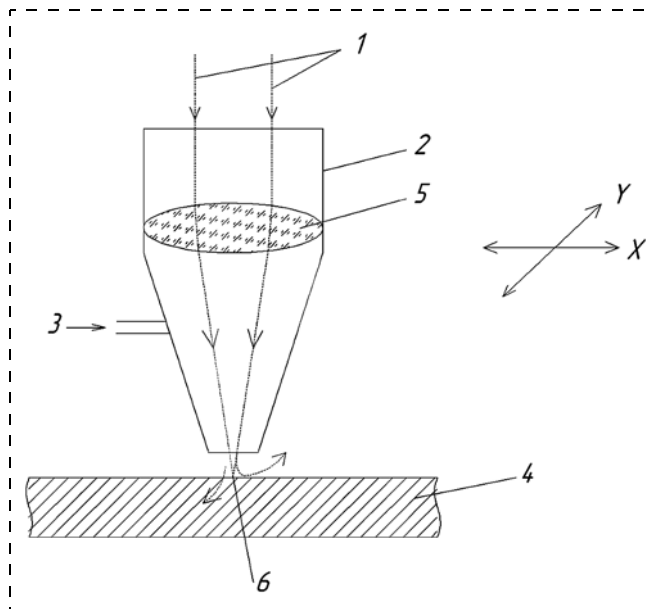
Схема лазерной плазмохимической резки: 1 — лазерный луч; 2 — защитный кожух режущей головки, совмещенный с объективом; 3 — вспомогательный газ; 4 — разрезаемый объект; 5 — линза; 6 — область расплава
